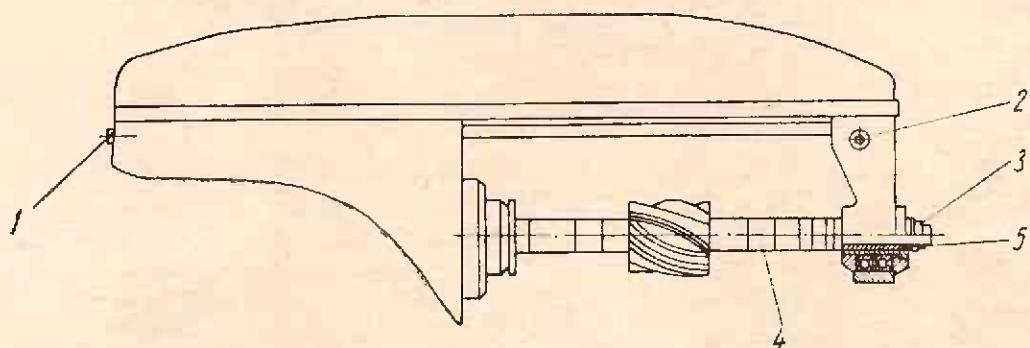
Схема установки инструмента на станках 6Н80 и 6Н80Г
